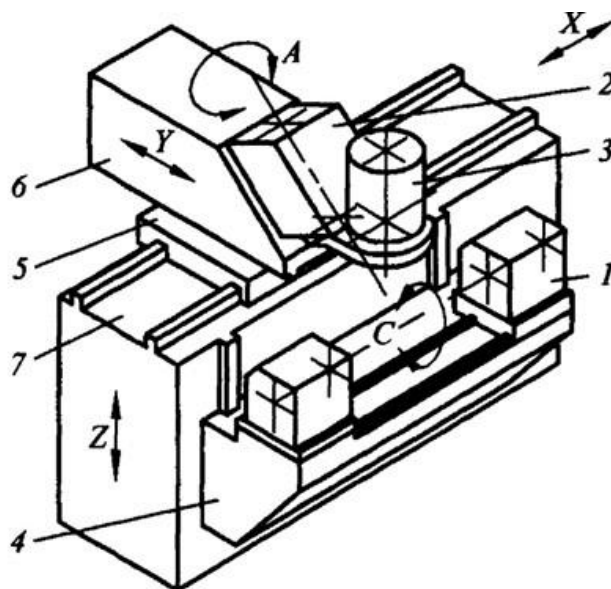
принципова схема верстату НХ-151 для кругової обробки лопатки: 1 – шпиндельні бабки кругової подачі заготовки; 2 – супорт кутового переміщення фрезерної головки; 3 – фрезерна головка; 4, 5, 6 – вертикальний, поздовжній і поперечний супорти верстату відповідно; 7 – станина.
